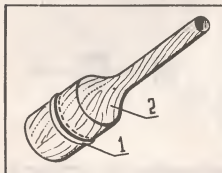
Простое приспособление для зачистки напайки на задирах зеркала цилиндра: 1 — поршневое кольцо с остро заточенной кромкой; 2 — деревянный толкатель с выточкой под кольцо (или старый поршень уменьшенного размера, насаженный на деревянную рукоятку).
